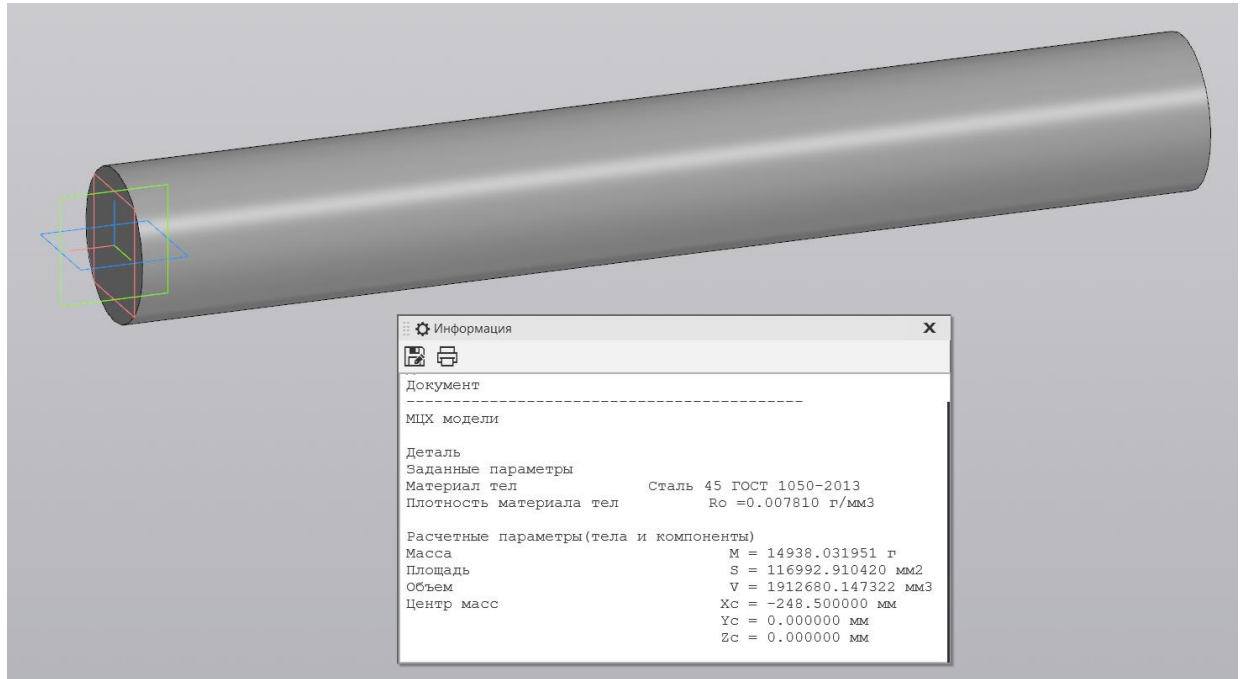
3D модель заготовки виготовленої з прокату
